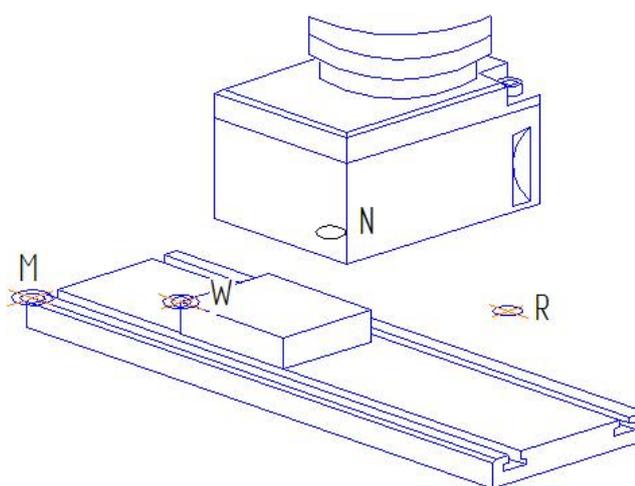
Базовые точки в рабочей зоне фрезерного станка с ЧПУ
